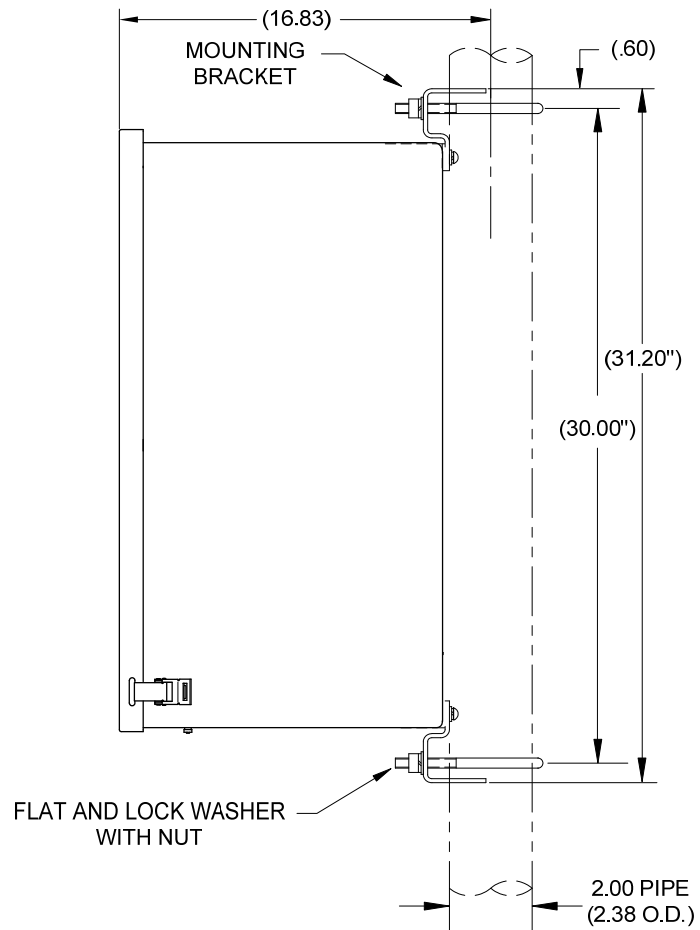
Instalação do invólucro 6800 no tubo de fixação
